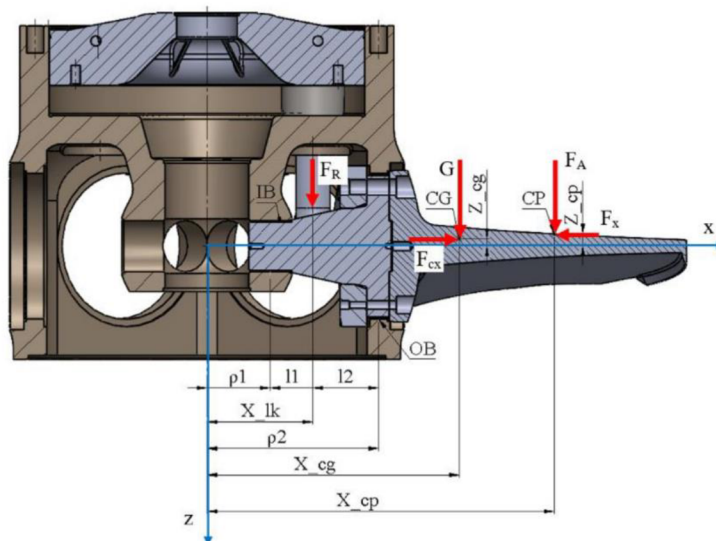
Detail regulačného mechanizmu rotorových lopatiek
